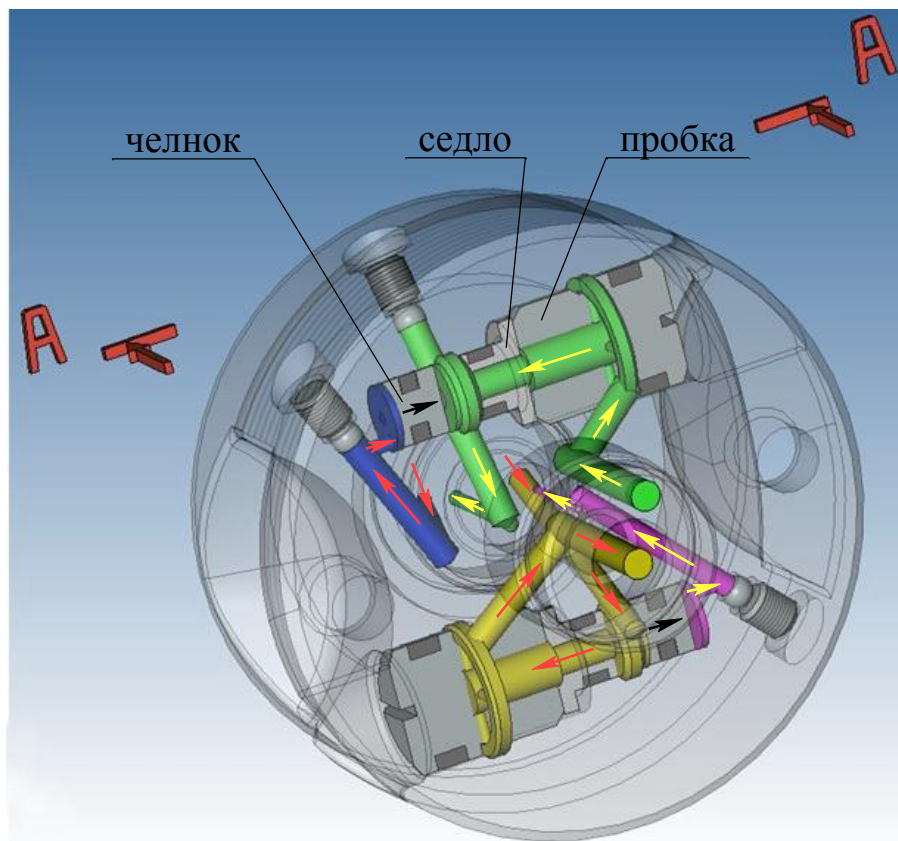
Эскиз корпуса гидрозамка для сведения ножей
